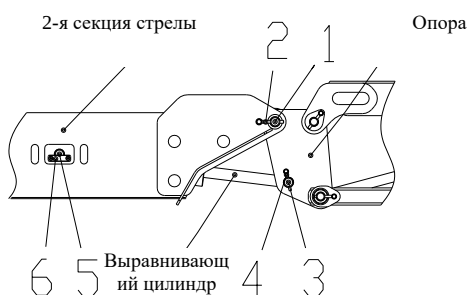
Схема демонтажа верхнего гидроцилиндра выравнивания
